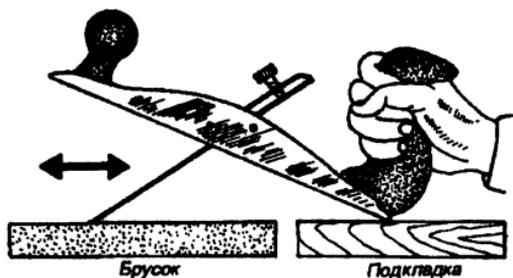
Способ заточки ножа рубанка под строго выдержанным углом
